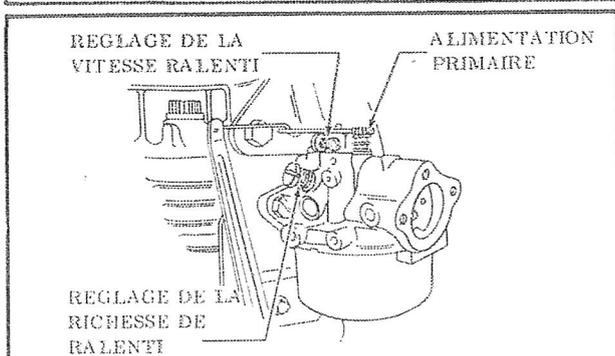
CARBURATEUR HORIZONTAL
